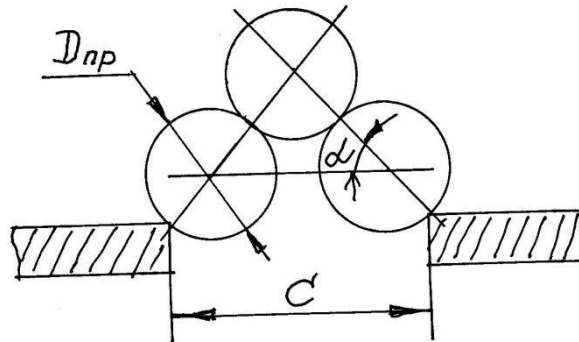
Розрахункова схема витікання ґрунтових агрегатів через зазор між планкою та барабаном
